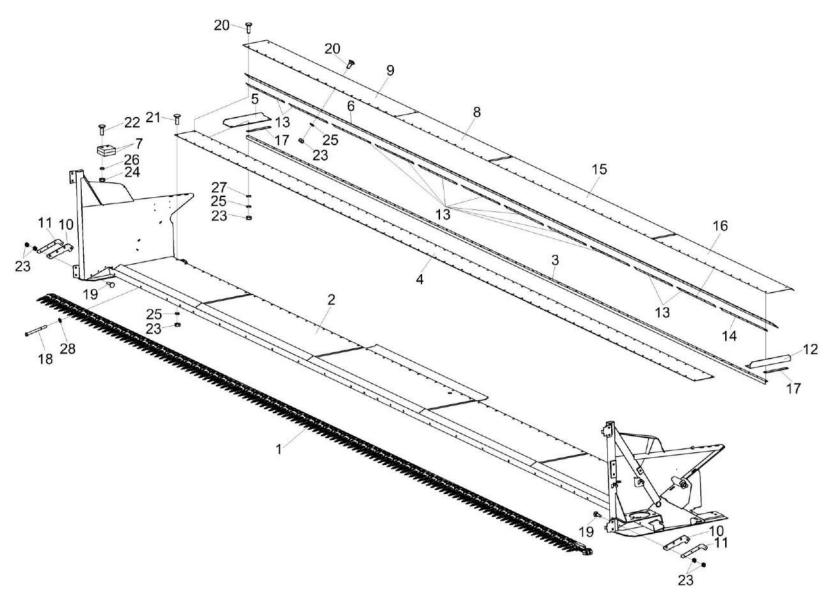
Приспособление для уборки рапса КЗК-9-1540000А (лист 2)
